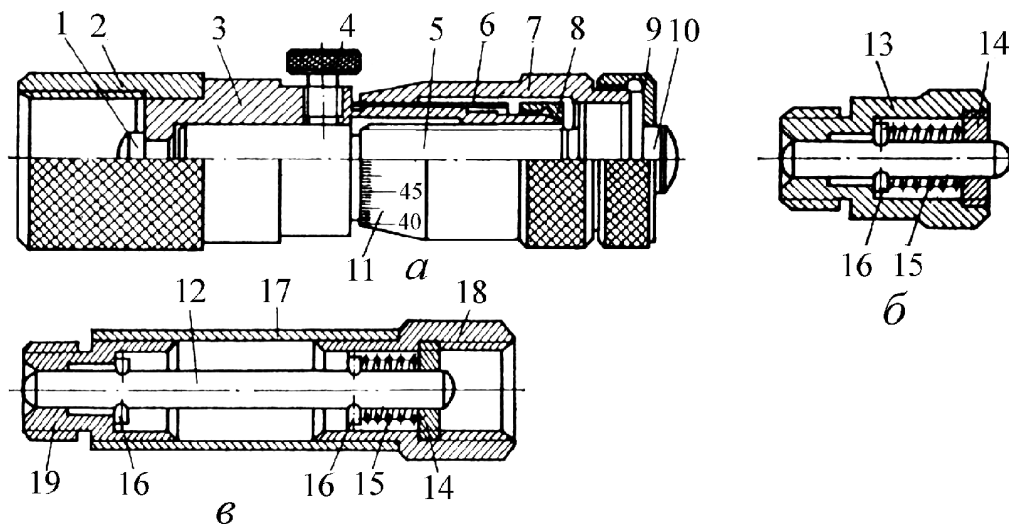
Конструкция микрометрической головки нутромера (а), защитного наконечника (б), удлинителя (в): 1 – измерительный наконечник; 2 – муфта; 3 – стержень; 4 – стопор; 5 – микрометрический винт; 6 – гильза; 7 – барабан; 8 – регулировочная гайка; 9 – затяжная гайка; 10 – микрометрический винт; 11 – круговая шкала; 12 – стержень; 13 – корпус; 14 – гайка; 15 – пружина; 16 – штифт; 17 – трубка; 18 – муфта с внутренней резьбой; 19 – муфта с наружной резьбой
